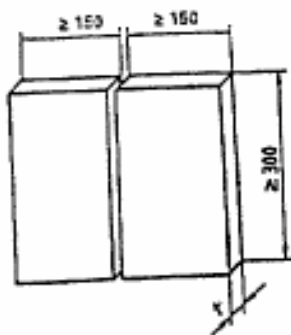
Dimensiunile probei pentru sudură cap la cap la tablă
